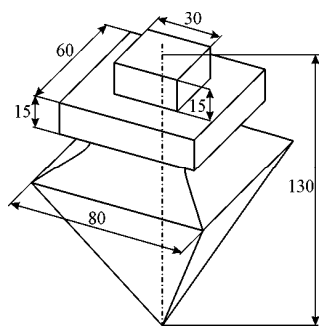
Схема вилівка «Опорний накопечник стійки конвеєра»
